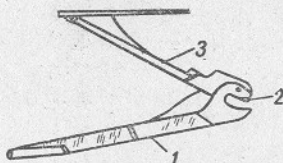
Крышка магази́нной коробки с подающим механизмом:
